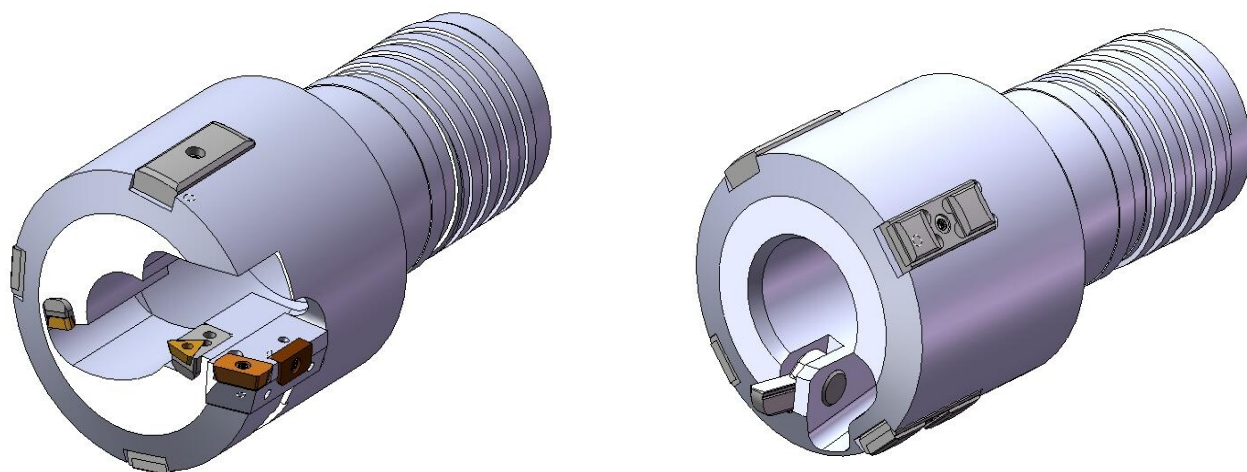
Головка кольцевого сверления и отрезная головка для отбора пробы  $\varnothing$  50 мм на большой глубине
